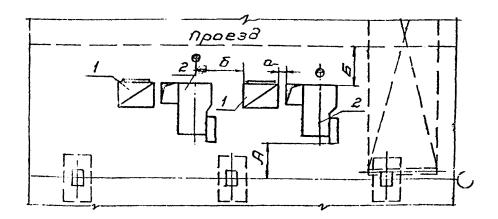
Схема расположения штамповочних линий на базе ГКМ: I - нагревательная печь; 2 - горизонтально-ковочная машина.
